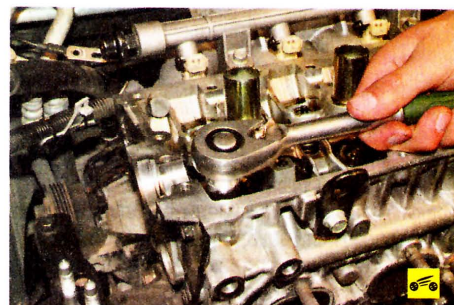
Порядок выворачивания болтов крепления головки блока цилиндров
